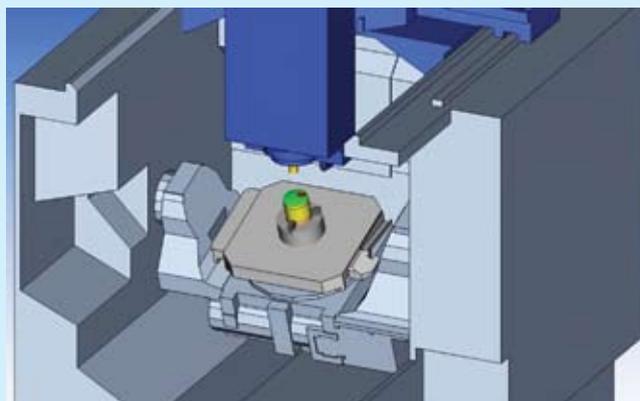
Пример компоновки вертикального фрезерно-токарного обрабатывающего центра, поддерживаемого в PartMaker 2015
